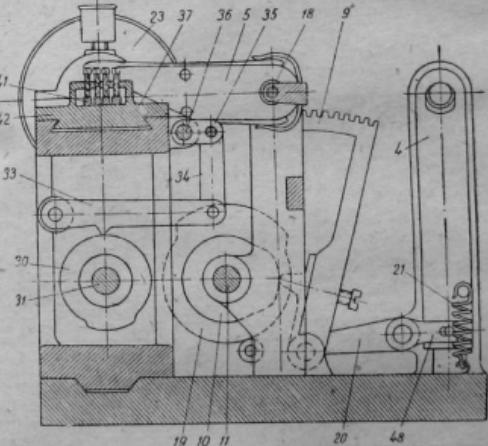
Схема токарного автомата 1-го часового завода для обточки барабанов (вид сбоку).
